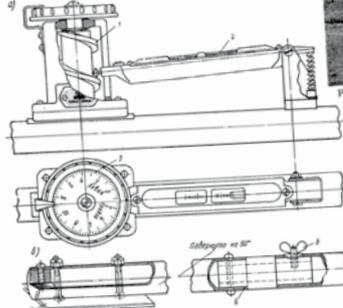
основные части прибора для измерения планировки участка; 1 — измерительное устройство инвариационного шаблона ШИД; 2 — часть шаблона; 3 — уровень; 4 — деталь; 5 — уровень; 6 — коррозийная трубка; 7 — барометр; 8 — уровень; 9 — барометр
